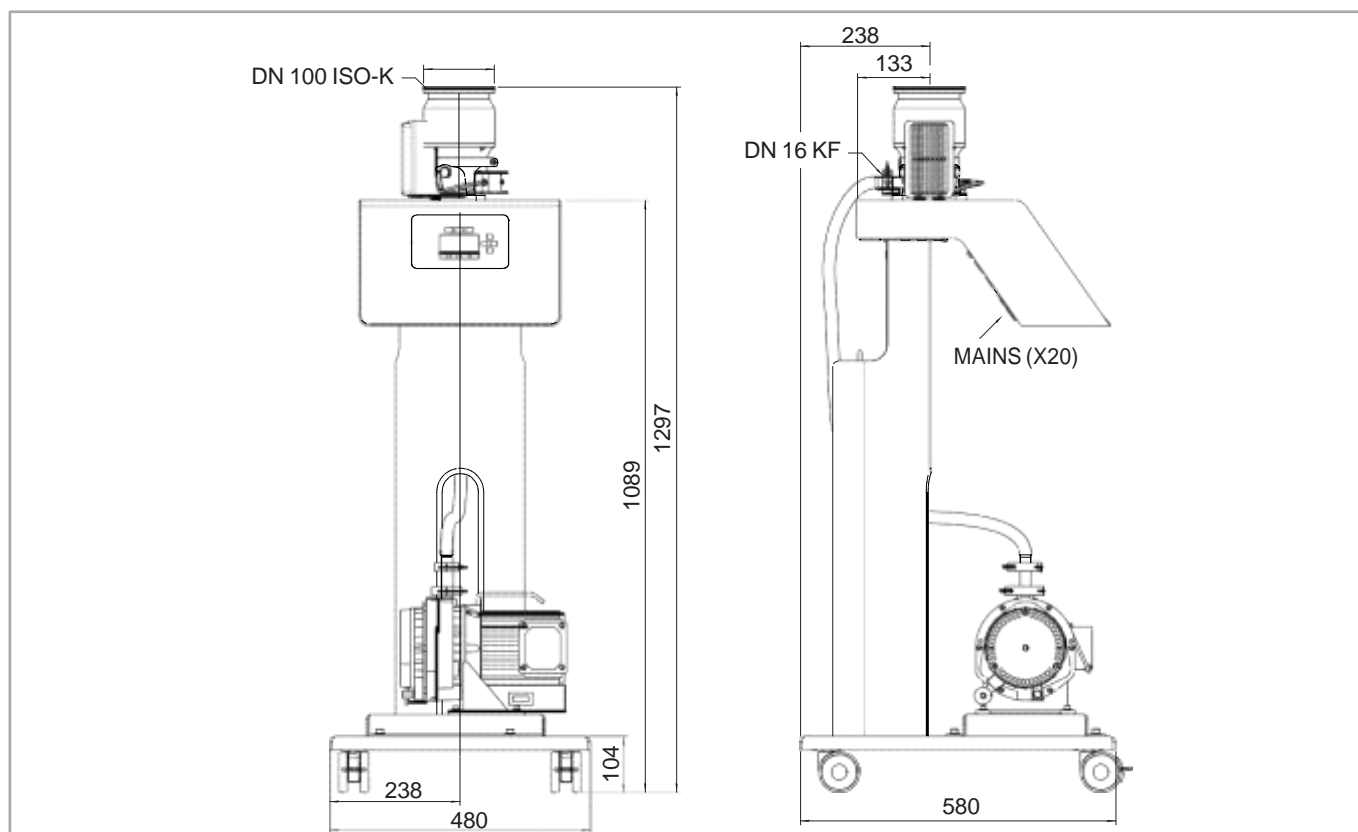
Габаритные размеры TURBOLAB 250 Cart, размеры в мм
